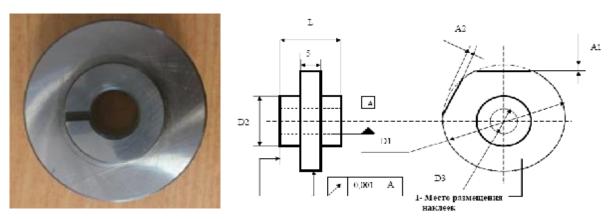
Внешний вид и эскиз мер для поверки межцентромеров
